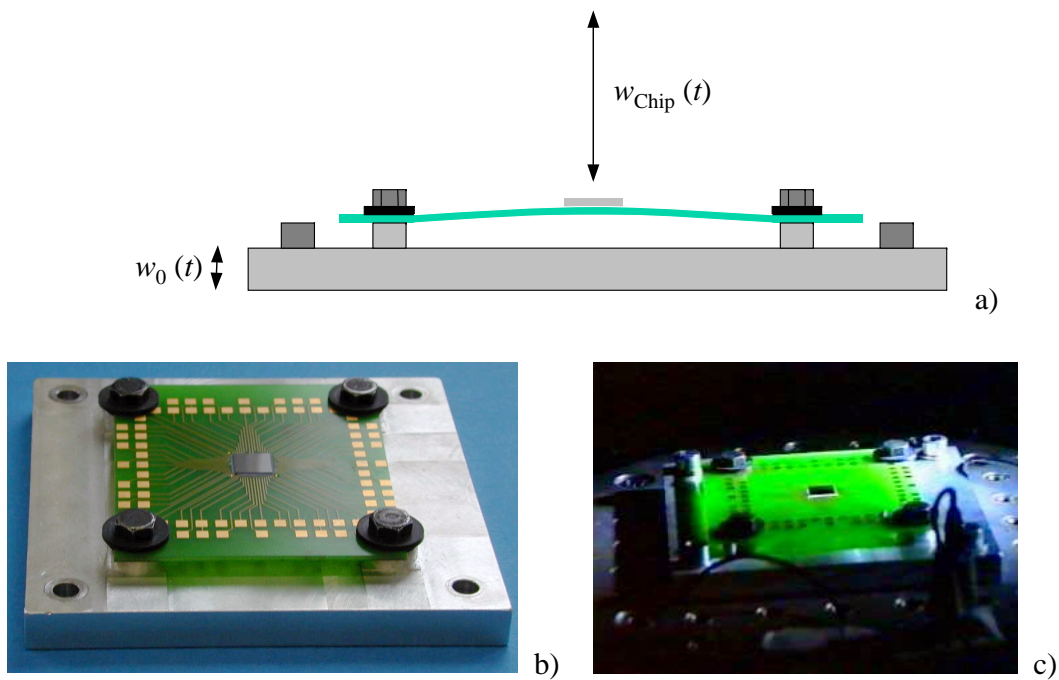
Vibrationstest: a) schematisch, b) Probenhalter mit Flip-Chip-Aufbau und c) Aufnahme des Tests unter stroboskopischer Beleuchtung
